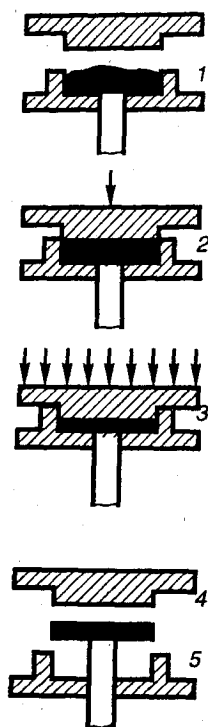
Схема прямого прессования: 1 — загрузка пресс-материала; 2 — замыкание формы; 3 — формовка под давлением; 4 — размыкание формы; 5 — готовое изделие
